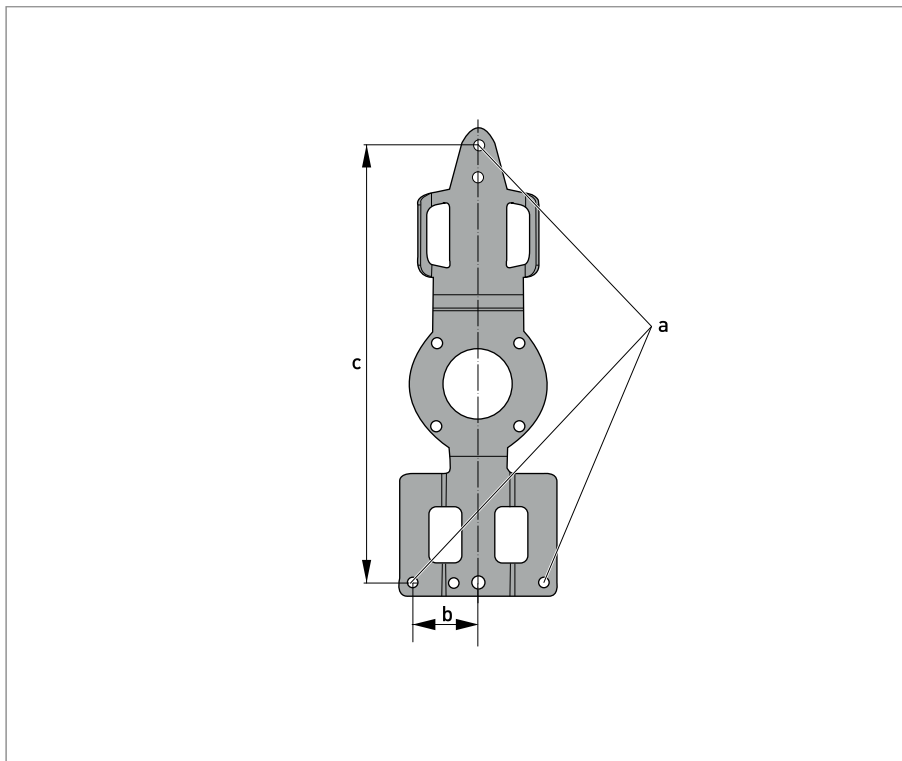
Abmessungen der Montageplatte für die Wand-Ausführung, Edelstahlgehäuse
